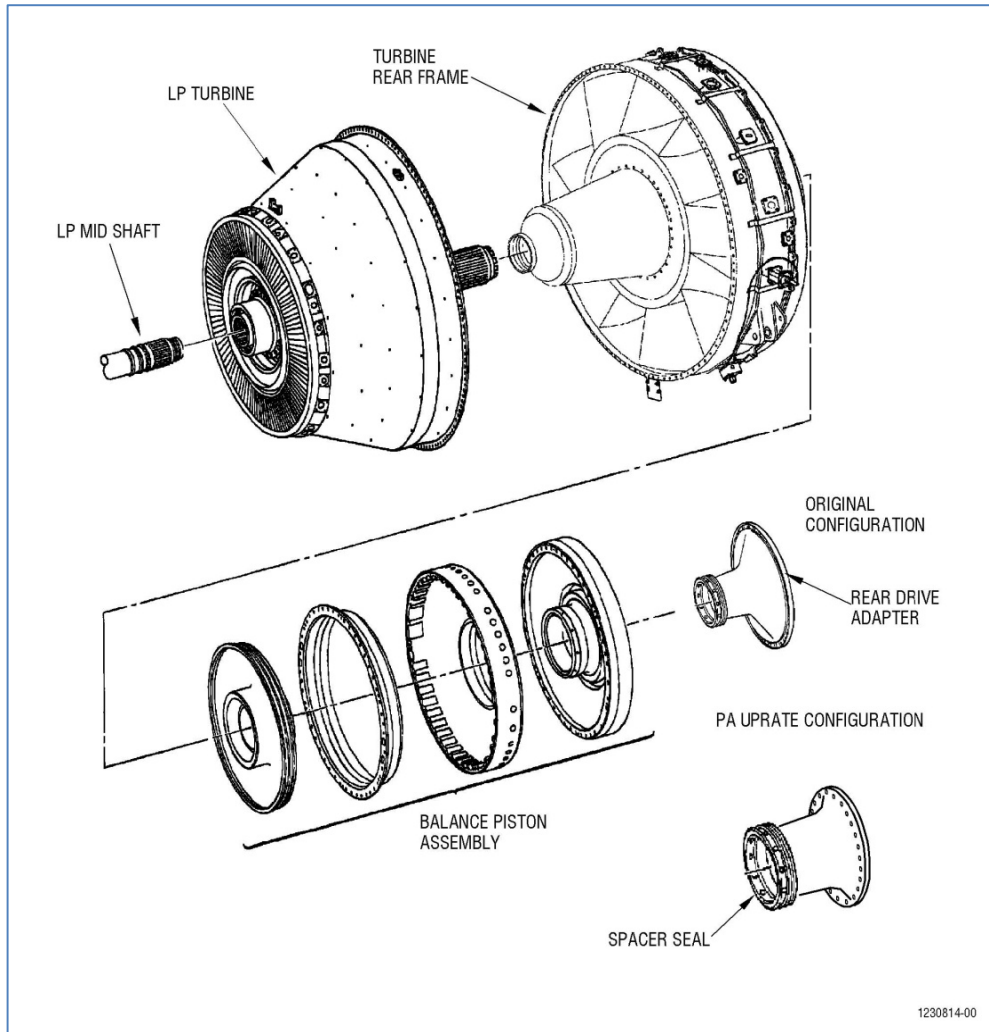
C. COMPONENTES PRINCIPALES DE UNA TURBINA A GAS
